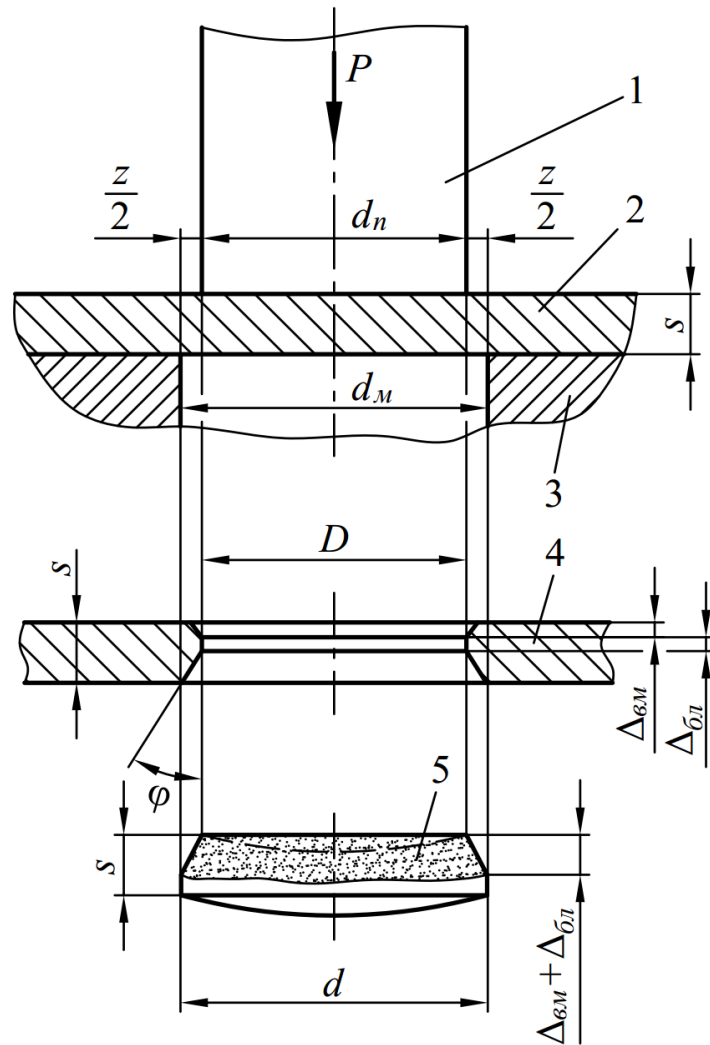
Схема процесу пробивання-вирубівання й похибки деталей після штампування:
